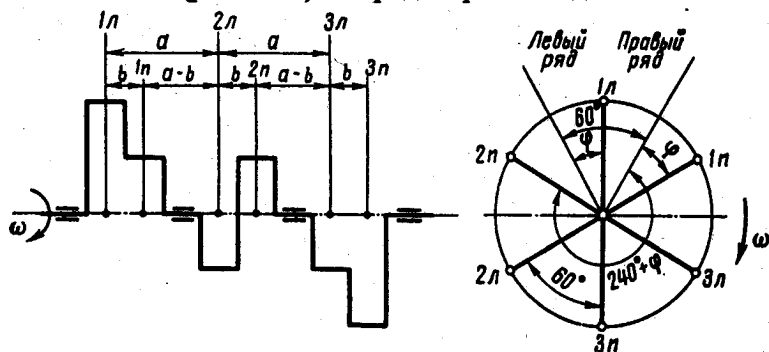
Схема шестицилиндрового V-образного двигателя с углом развала цилиндров 60°
